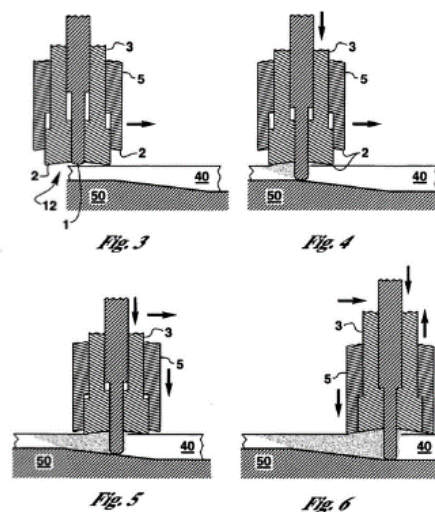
Desenho da ferramenta de SFL com o pino ajustável.
